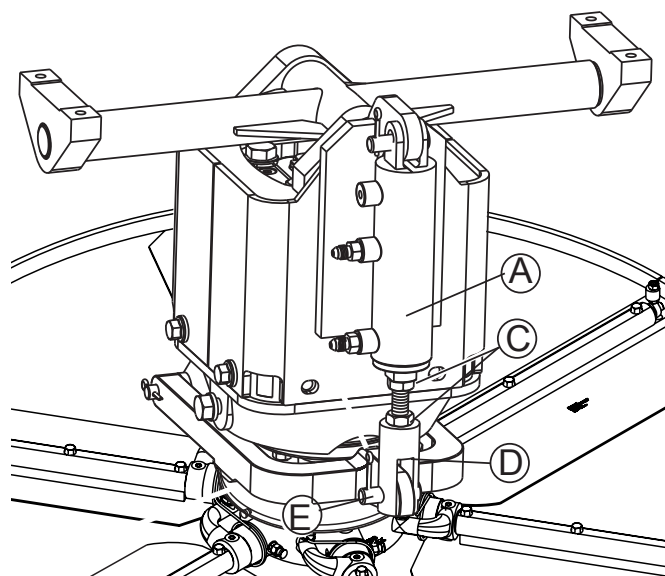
Réglage de la hauteur du bord d'attaque de la lame
